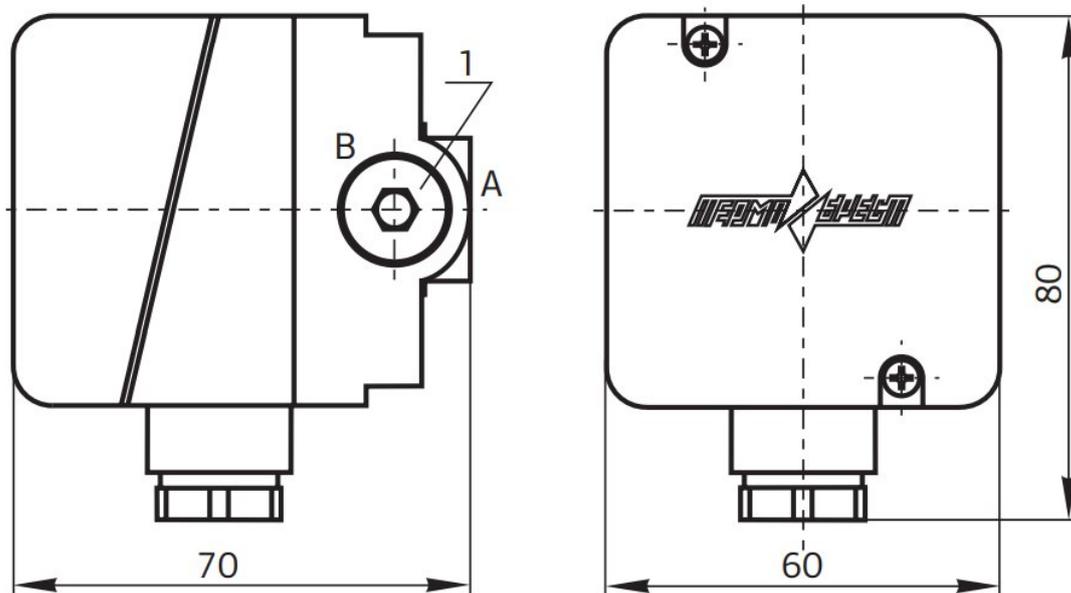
Габаритные размеры датчика-реле избыточного давления ДРД
